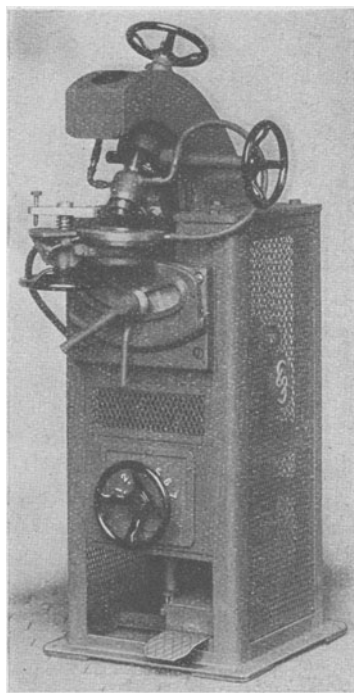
Elektrische Edelstahlaufschweißmaschine.
